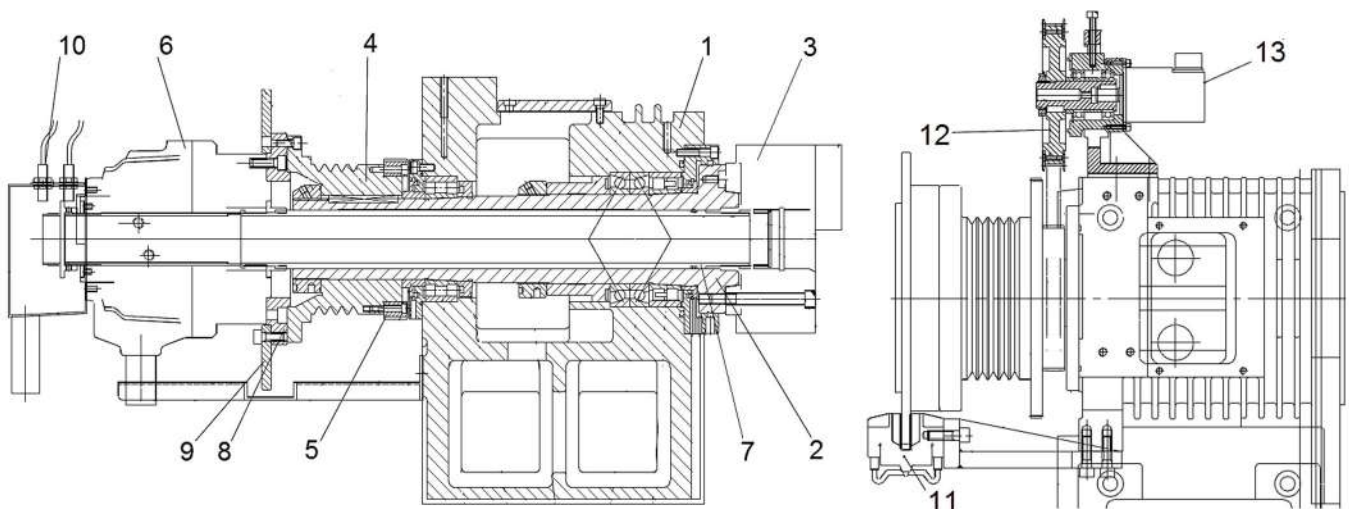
Шпиндельний вузол токарного верстата з ЧПК
